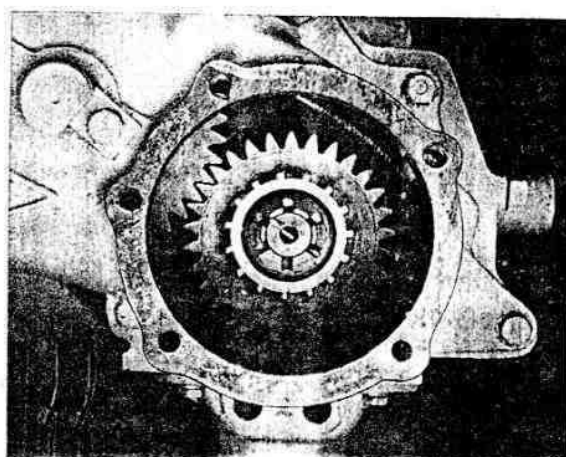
Detalle de la instalación del engranaje de mando de la caja de transferencia, acoplado en el engranaje intermedio.
